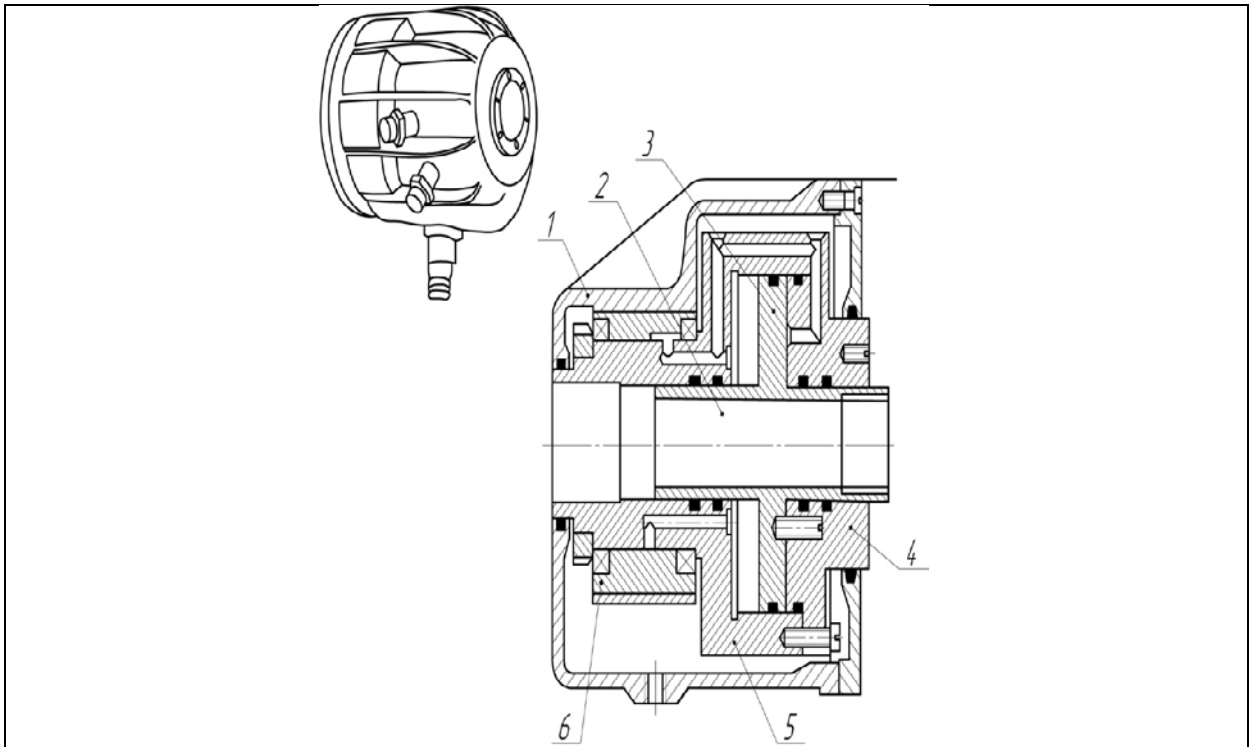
Гідравлічний циліндр, що обертається: 1-кожух; 2-шток; 3-поршень; 4-фланець; 5-корпус; 6-гідравлічна муфта
